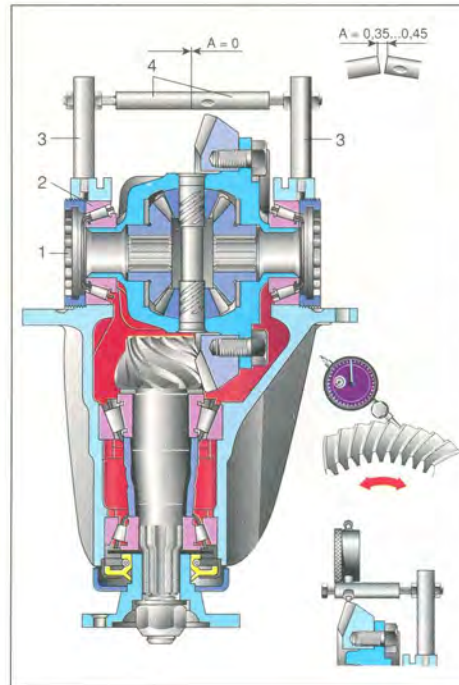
Приспособление для контроля предварительного натяга подшипников дифференциала: 1 – регулировочная гайка; 2 – подшипник; 3 – стойка приспособления; 4 – стержни.
